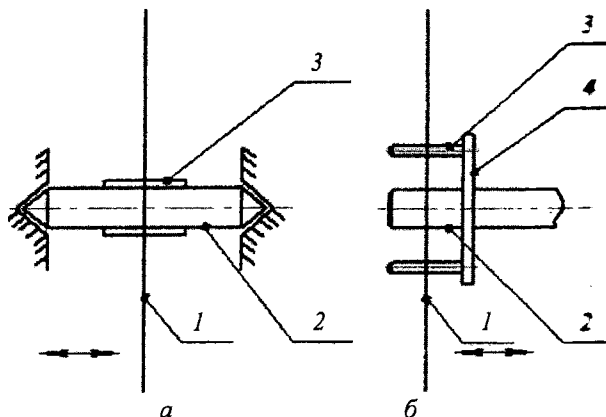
Варианты установки заготовки распиловочного диска с использованием шпонок (а) и штифтов (б)
